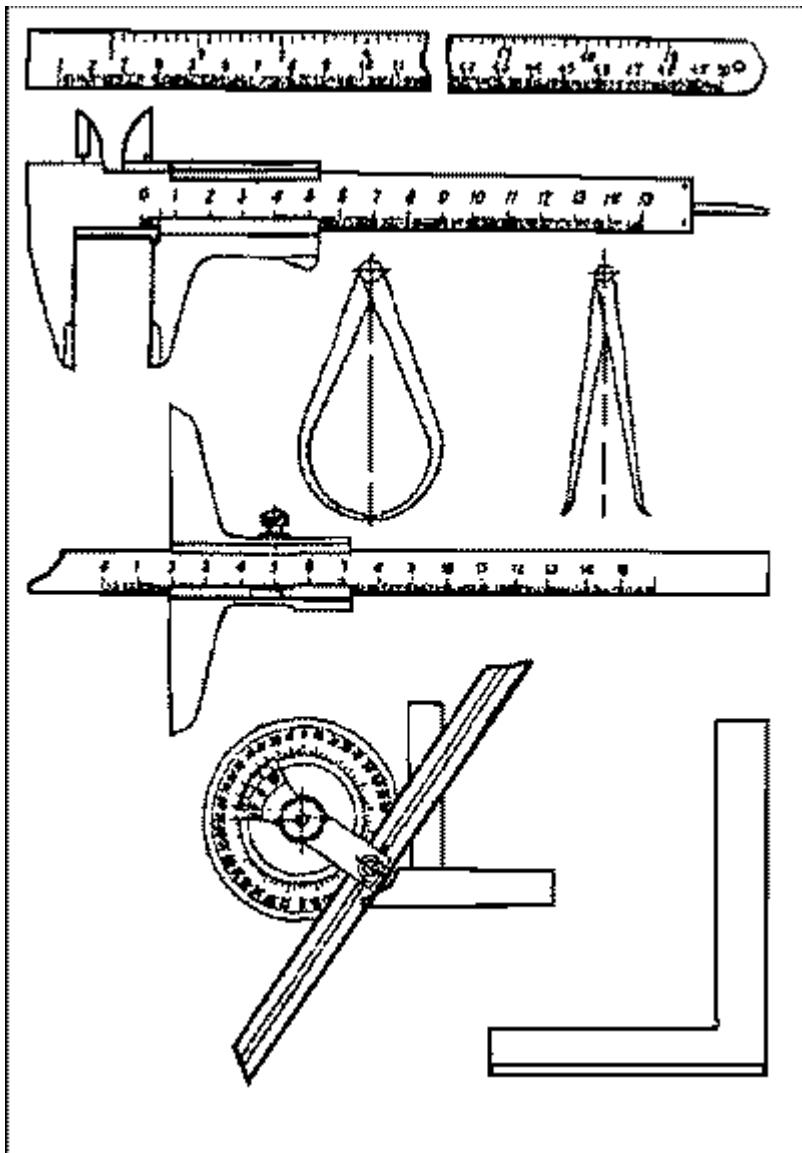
Универсальные измерительные инструменты: а – мерная металлическая линейка; б -штангенциркуль; в – кронциркуль нормальный; г – нутромер нормальный д – штангенглубиномер; е – угломер универсальный; ж – угольник плоский на 90°
